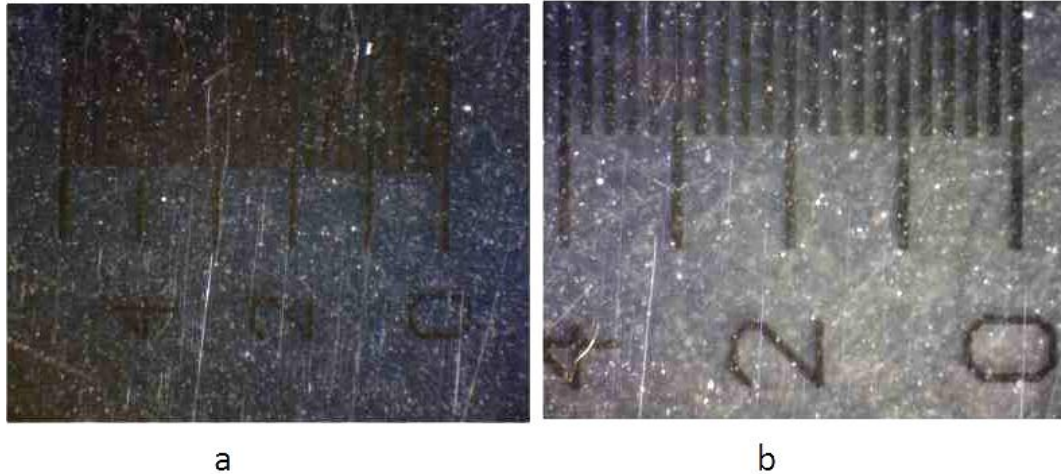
Snímky z mikroskopu vzorku 8 obráběného laserem - materiál 11 375
